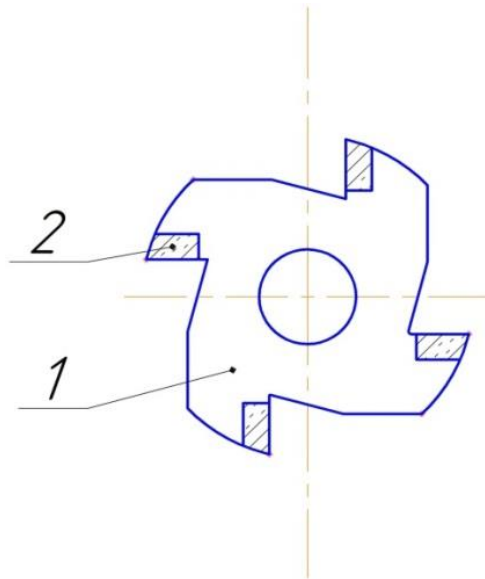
Круглый фасонный резец, с напаянными твердосплавными пластинками:
